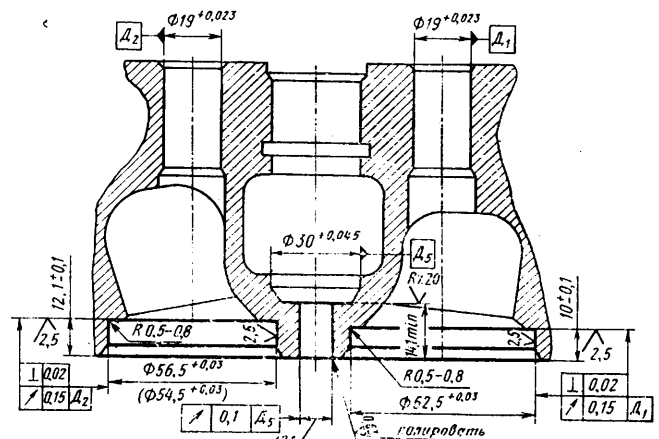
Расточка гнезд под ремонтные седла и обработка отверстия под расширитель форсунок
